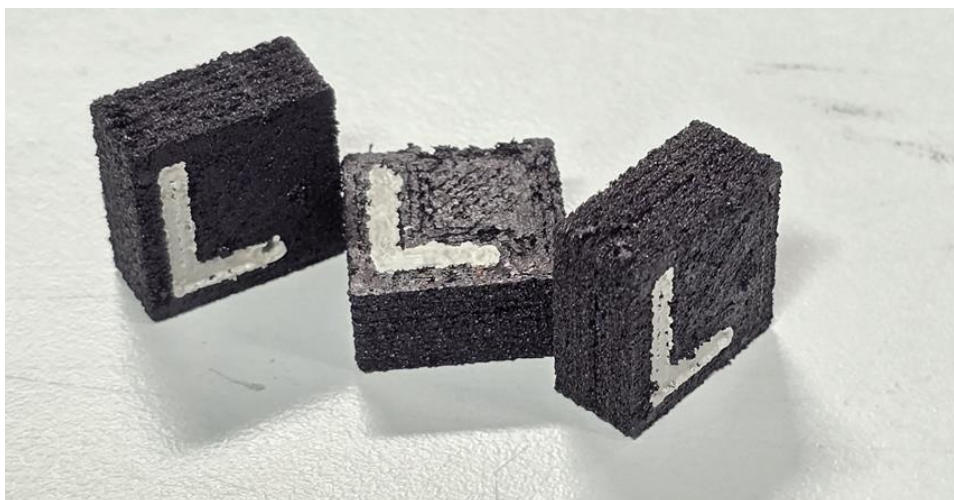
Gedruckter Produktdemonstrator mit integrierter Spule
